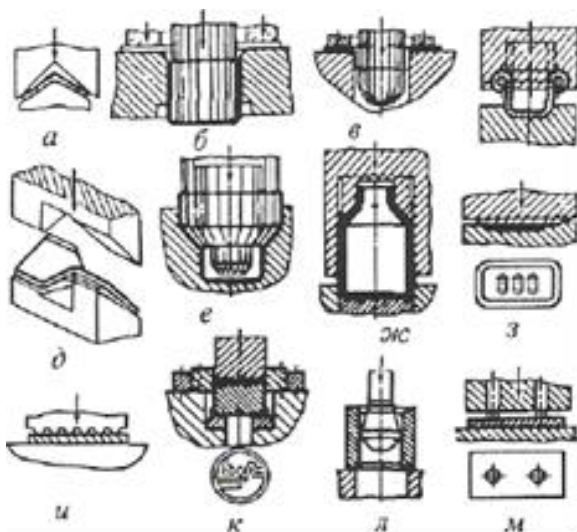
Схема формоизменяющих листовых операций: а - гибка; б - вытяжка; в - отбортовка; г - закатка; д - скручивание; е - раздача; ж - обжим; з - формовка; и - правка; к - чеканка; л - калибровка; м - кернение.
